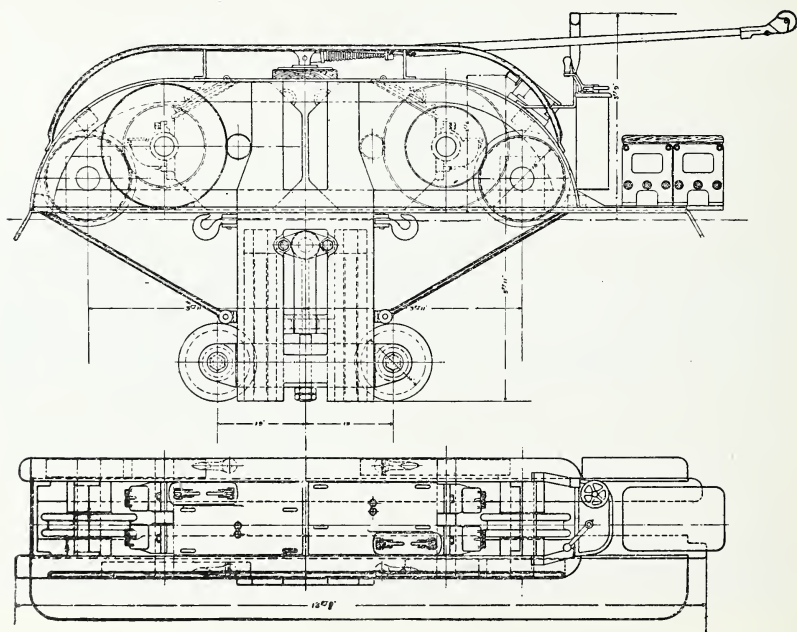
Elévation et plan tracteur électrique 100 chevaux.
